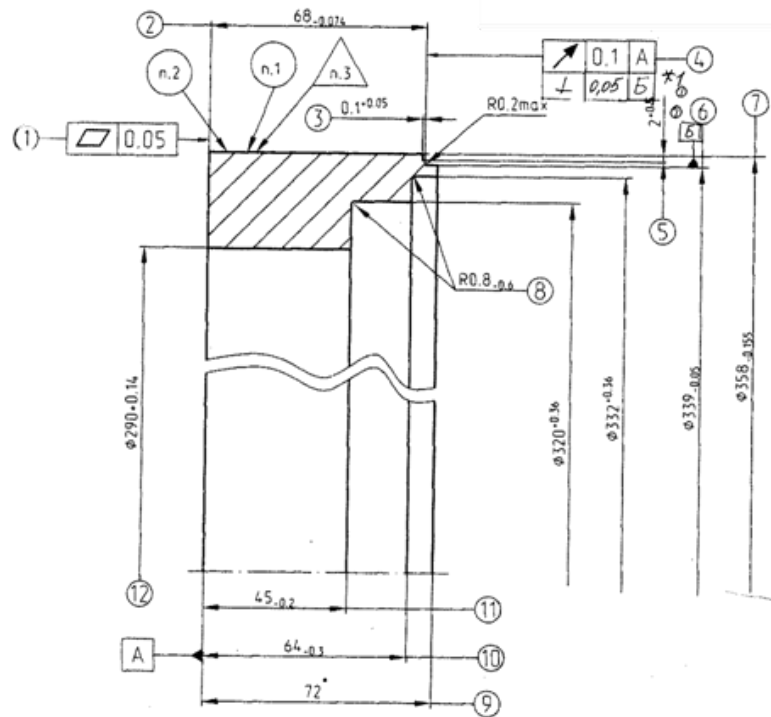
Механічно оброблена заготовка 1001-6602 під зварювання ЕПЗ.
